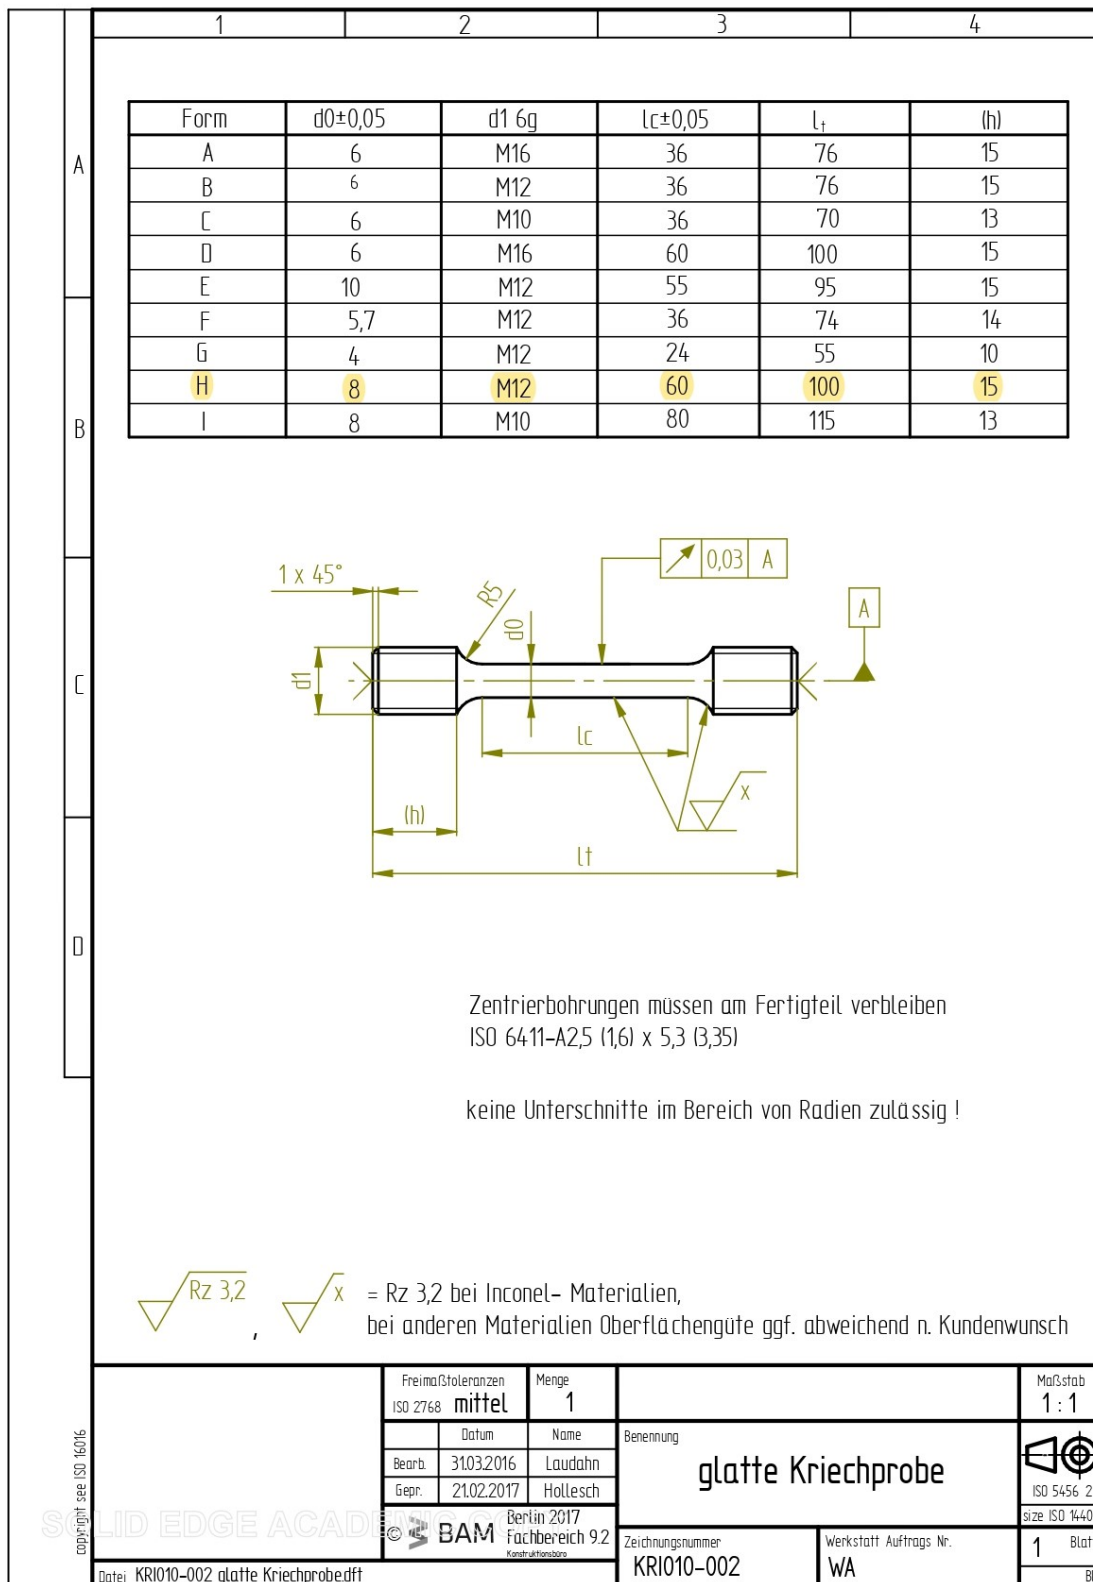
Technische Zeichnung Kriechproben (Form H).
